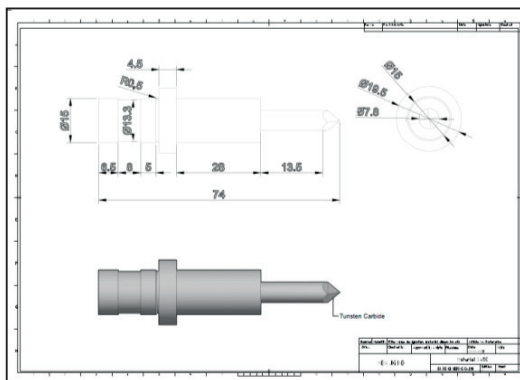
รูปเครื่องมือจับยึด (Jig & Fixture) แบบเดิม
